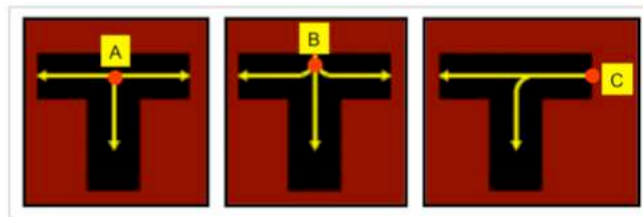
Llenado del molde no equilibrado. Fuente: ECL
